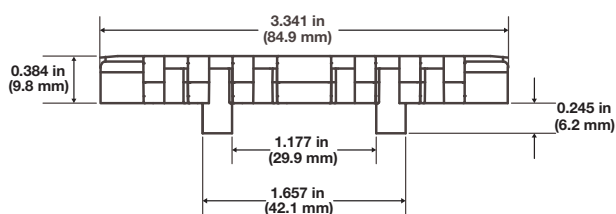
Série 900 Flat Top 85 mm moulé à la largeur
